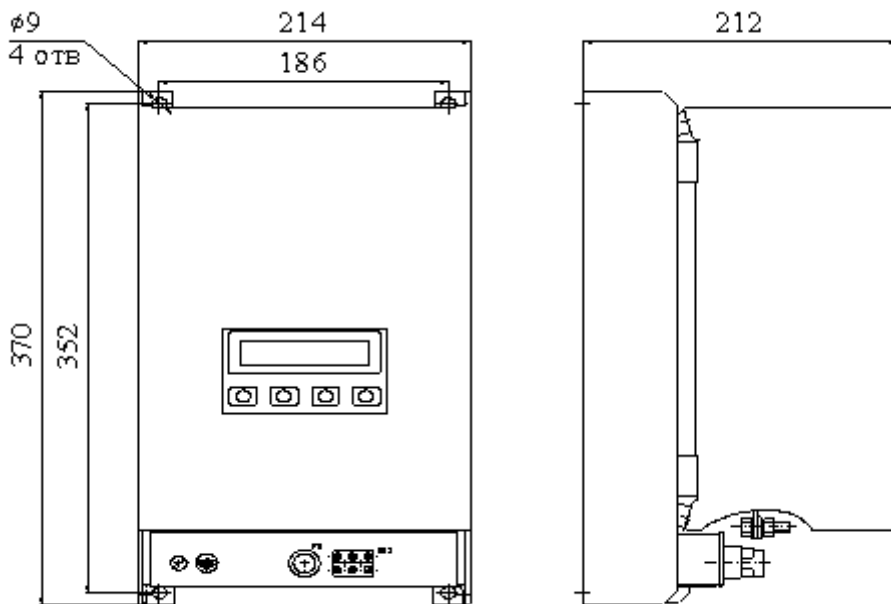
Габаритные и установочные размеры УПП1-Х7Х
